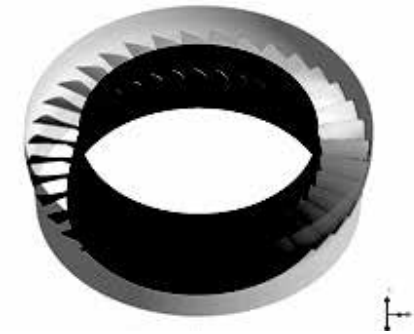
Робоче колесо осьового компресора Rotor 37
